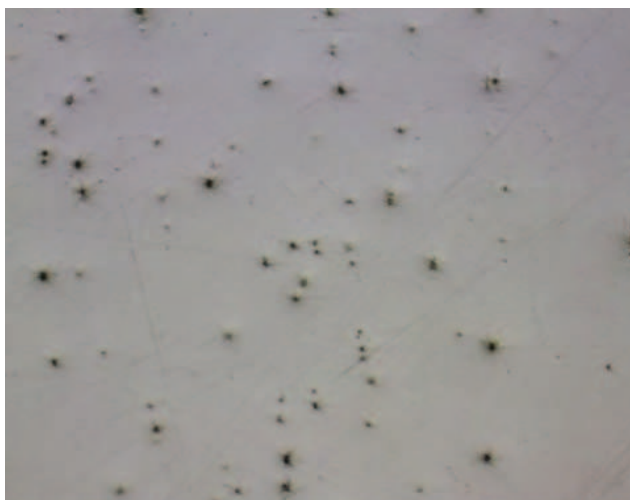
Область пористости в отливке жаропрочного никелевого сплава [8]
